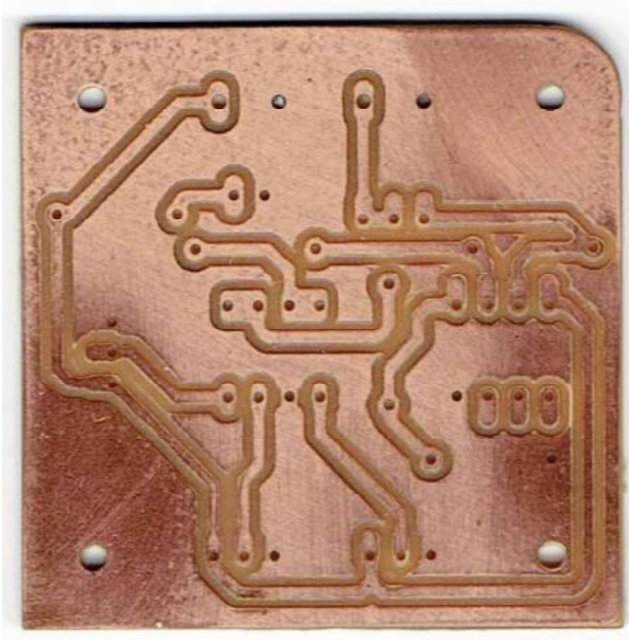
Prototipo PCB de la tarjeta KIT INST-01.
